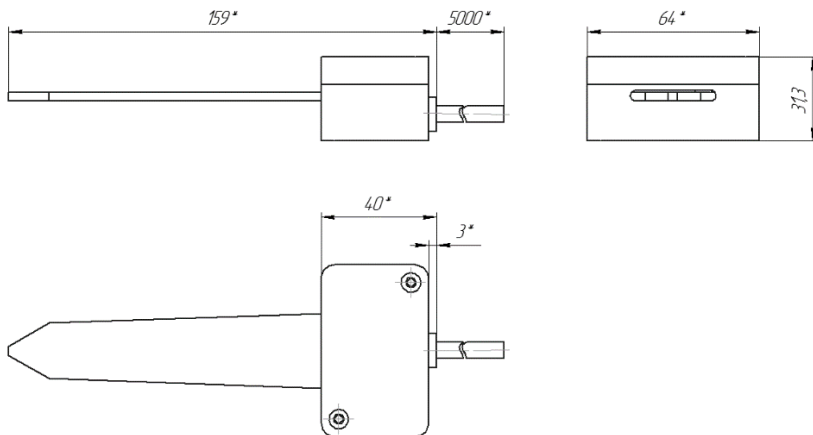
Габаритные размеры изделия «СОКОЛ-ДВП».
